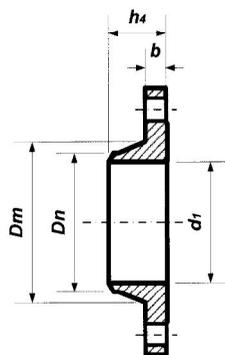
Конструкция и размеры фланца приварного встык по ГОСТ 12821-80 (к табл. 22)
